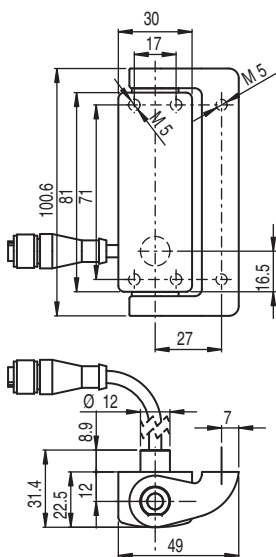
Dimensiones S400-Mx-CB02M12-W en mm
